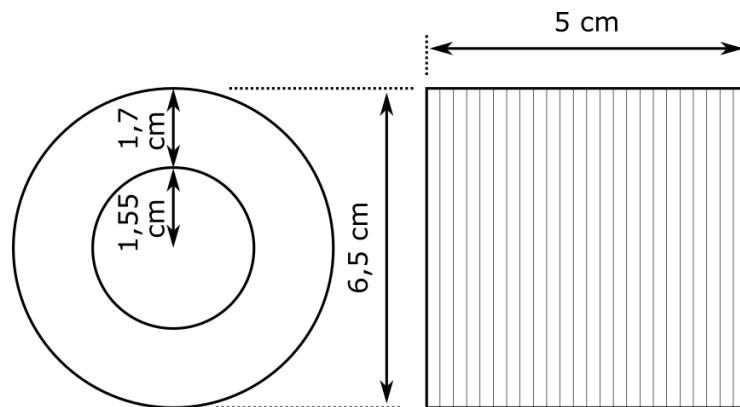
Dimensiunile bobinelor utilizate în releele NF cu două bobine [78]
